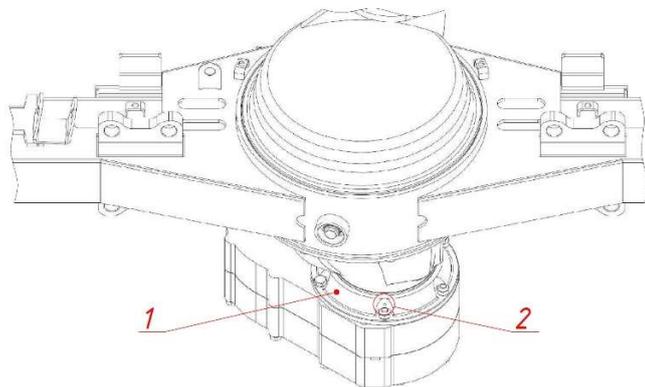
Расположение контрольного отверстия в нижней части фланца картера проходного редуктора
